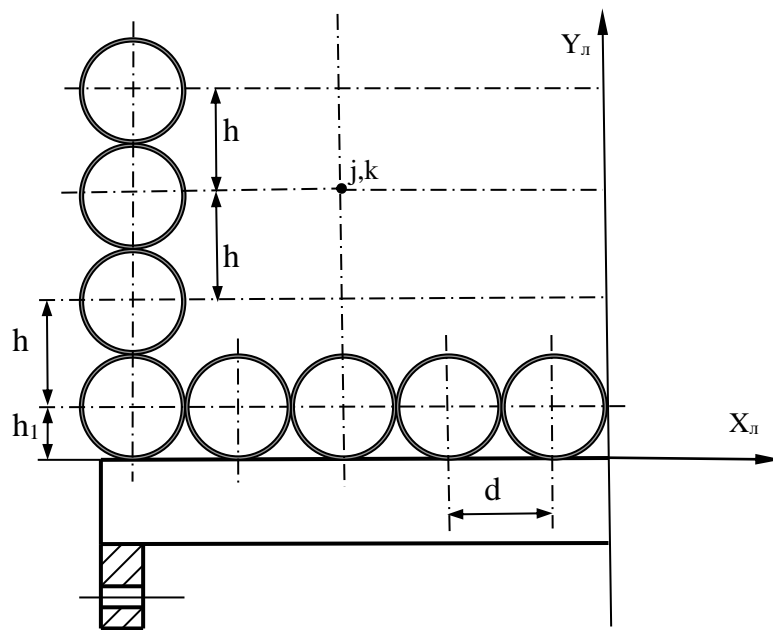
До визначення координат елементів пакету трубчастих направляючих.
